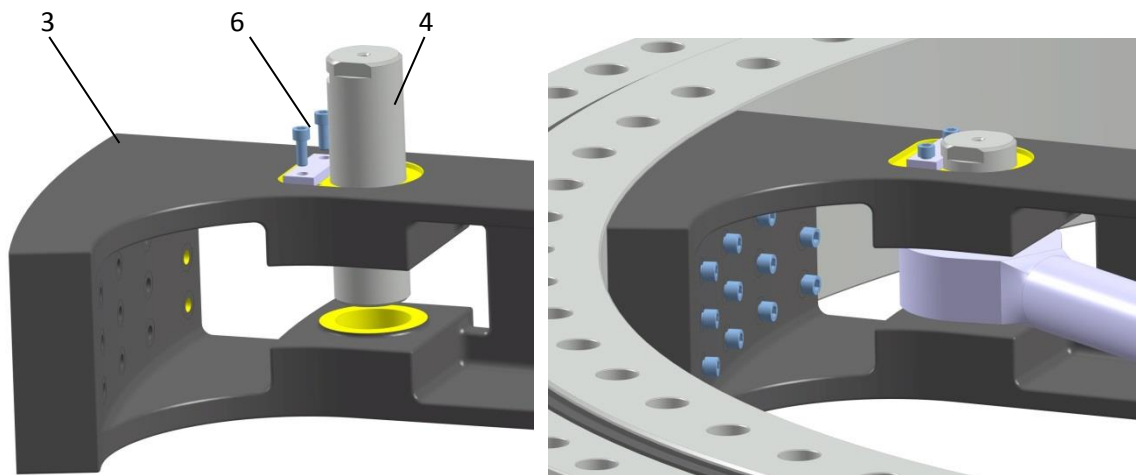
Befestigung der Zylinder am Pitchsteg und Montage im Blattlager
